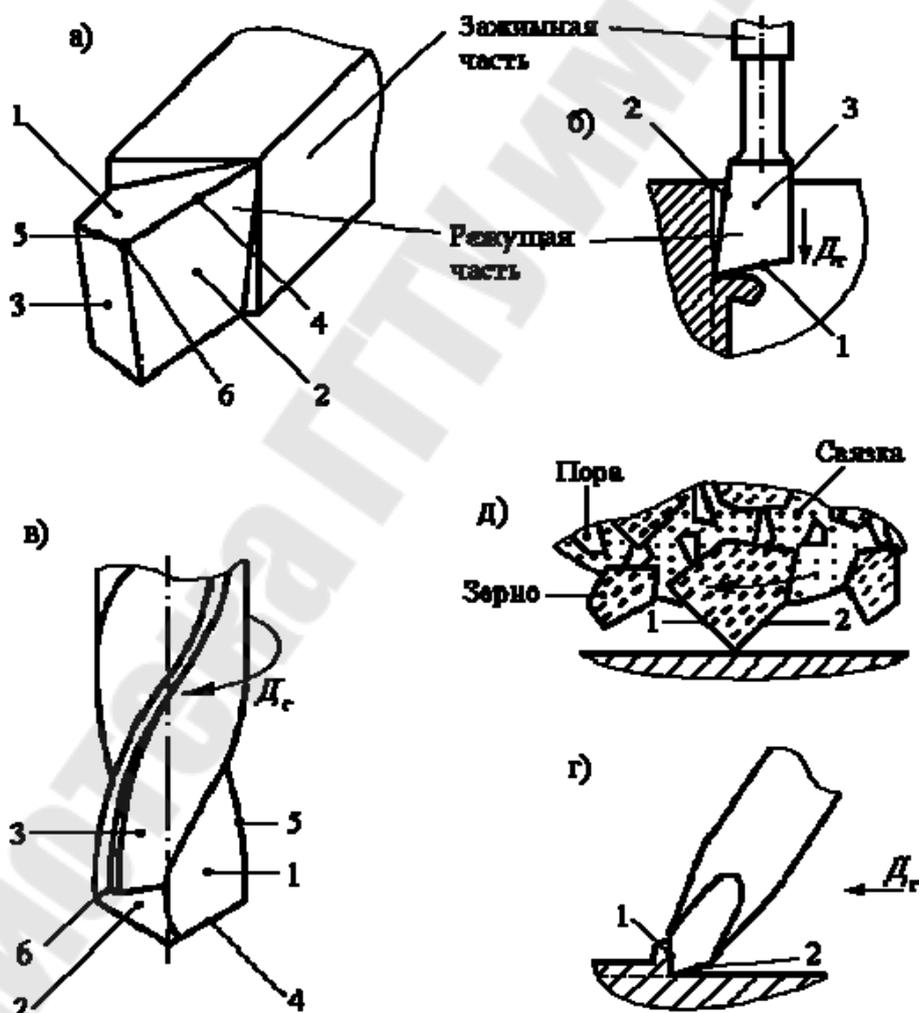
Составные части и рабочие поверхности инструментов: 1 – передняя поверхность, 2 – главная задняя поверхность, 3 – вспомогательная задняя поверхность, 4 – главная режущая кромка, 5 – вспомогательная режущая кромка, 6 – вершина режущего лезвия.
